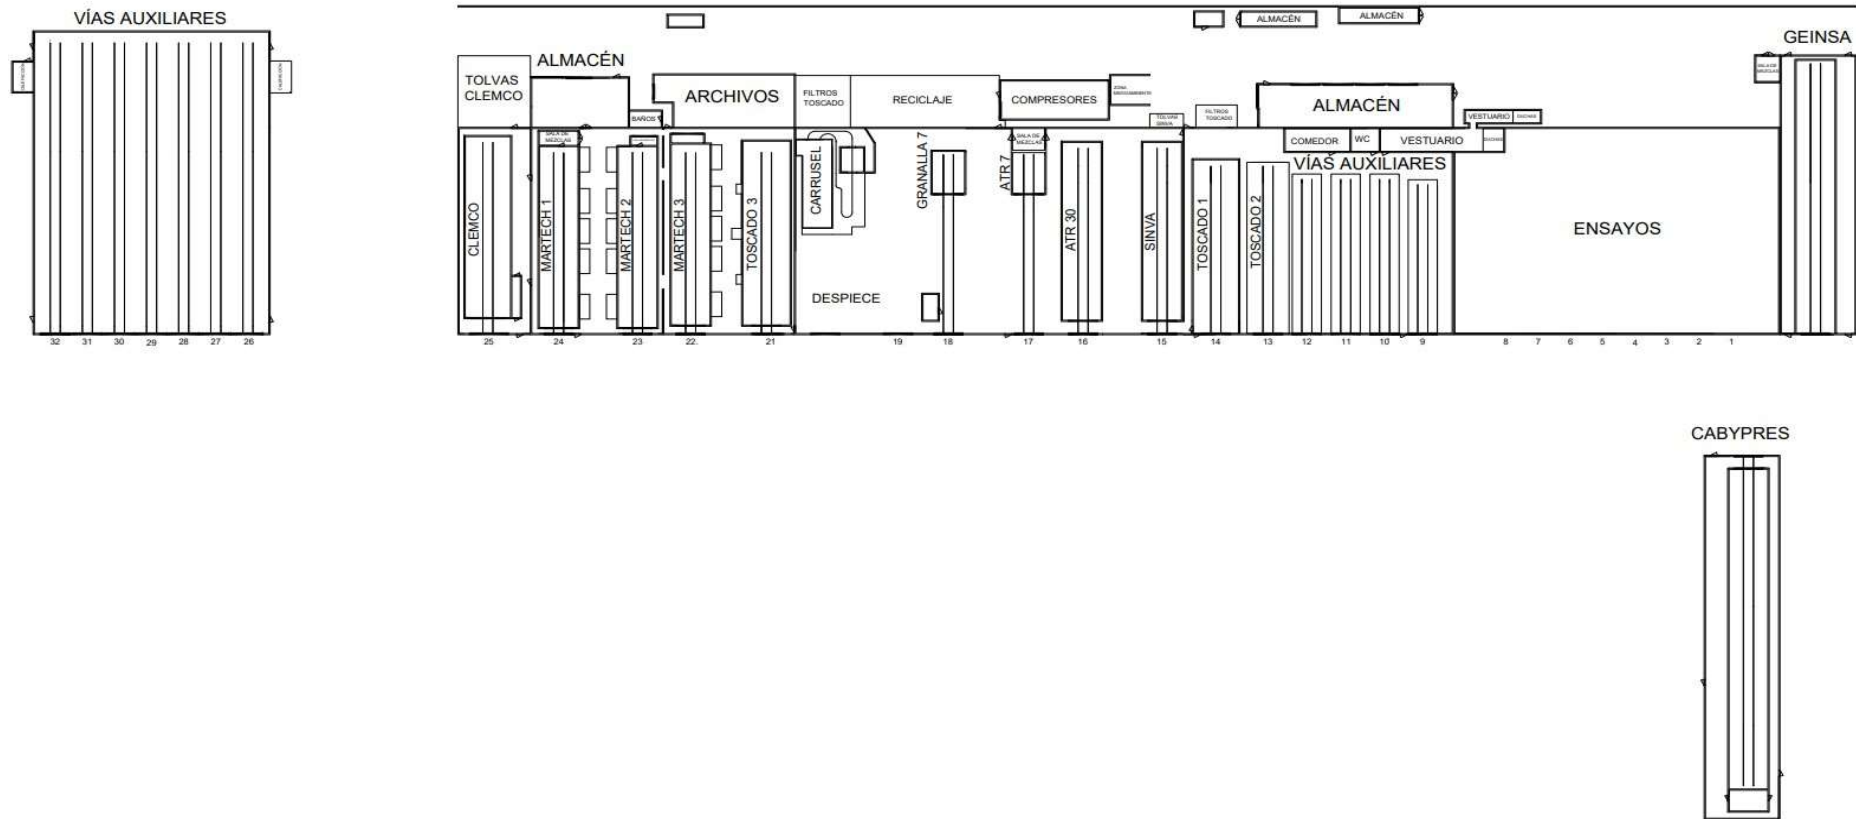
Distribución en planta de las naves de pintura. Fuente: Stadler Rail Valencia
